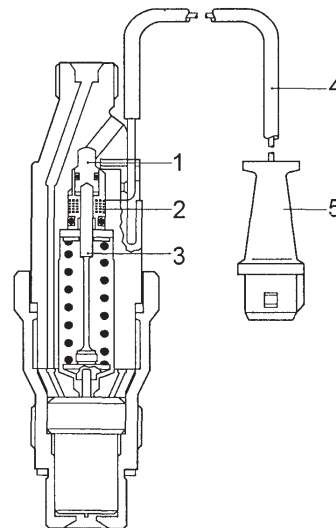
Схема форсунки с датчиками подъема иглы:
